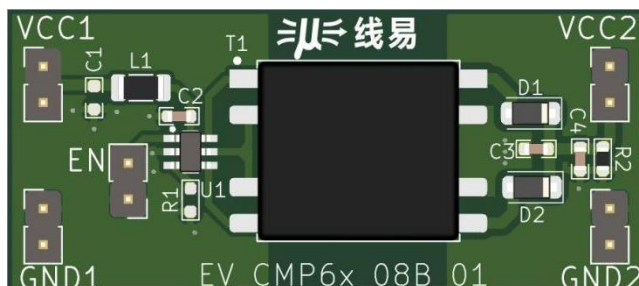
PCB 示意图(尺寸: 20x 45mm)
